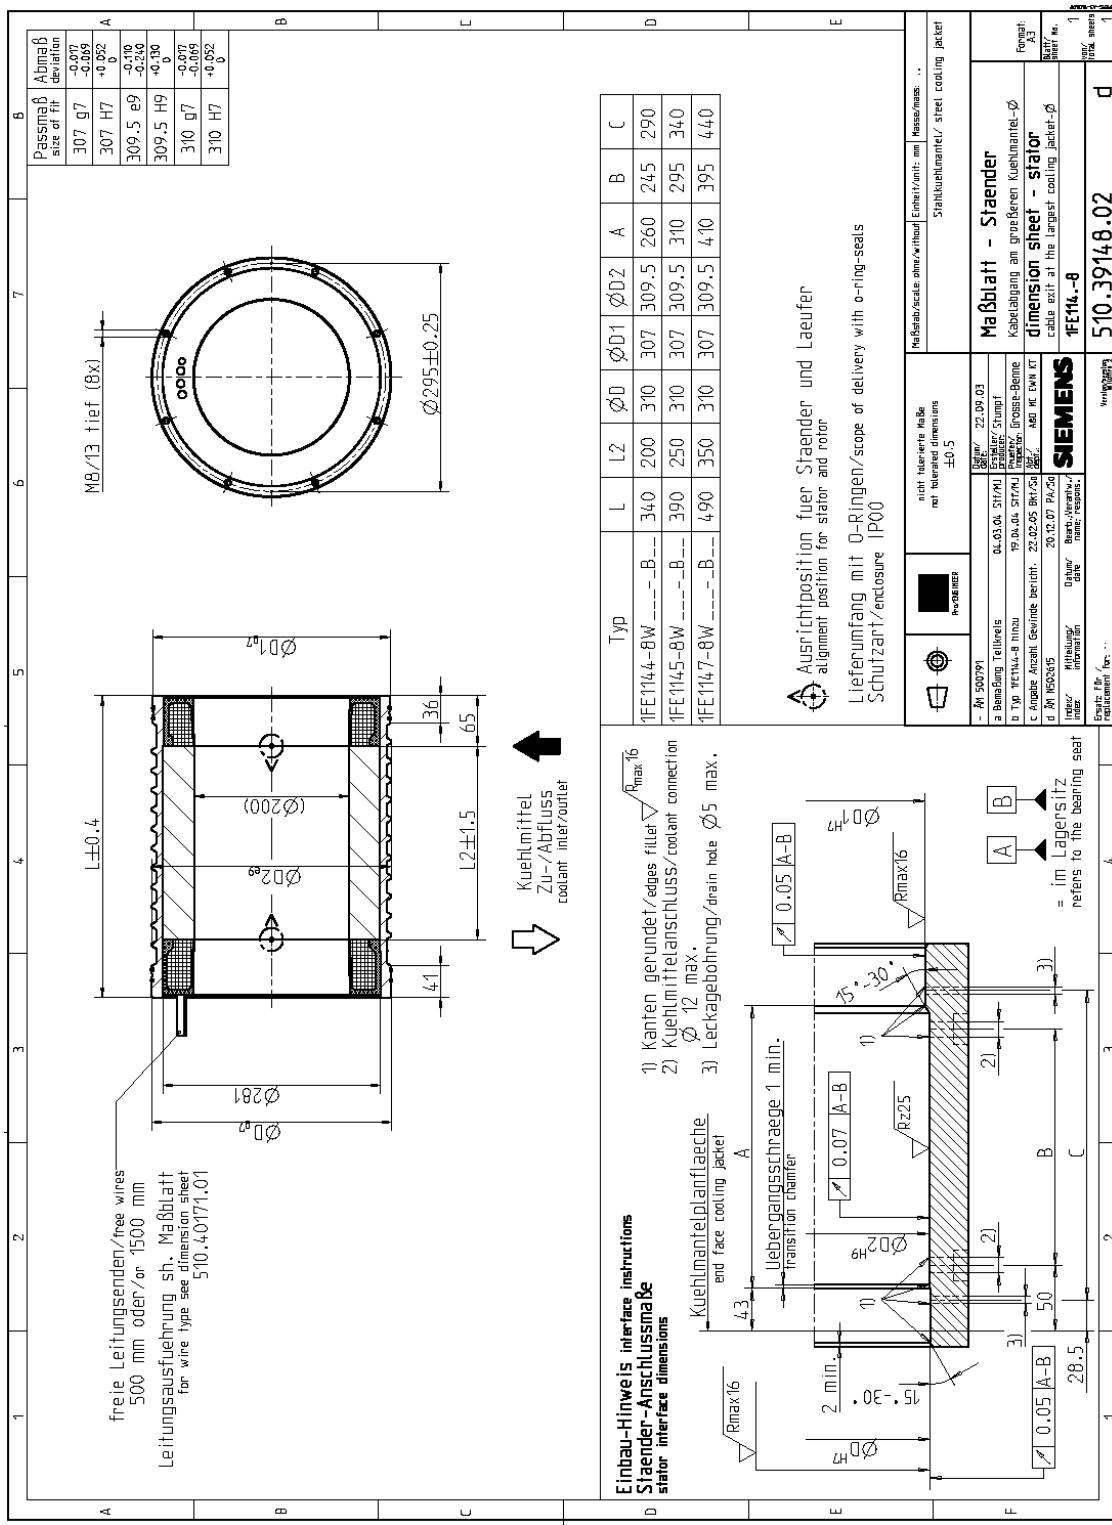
1FE114□-8, Ständer mit Kühlmantel, Kabelabgang am größeren Kühlmanteldurchmesser
